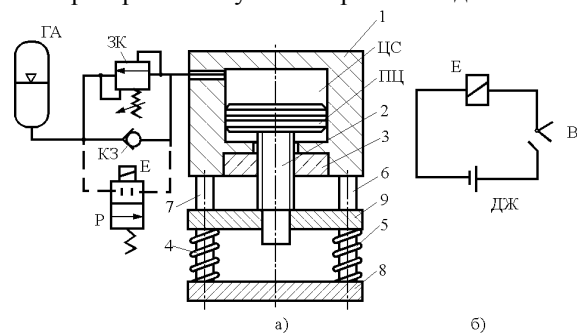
Принципова конструкція одноциліндрового пристрою –а; можлива електрична схема – б
